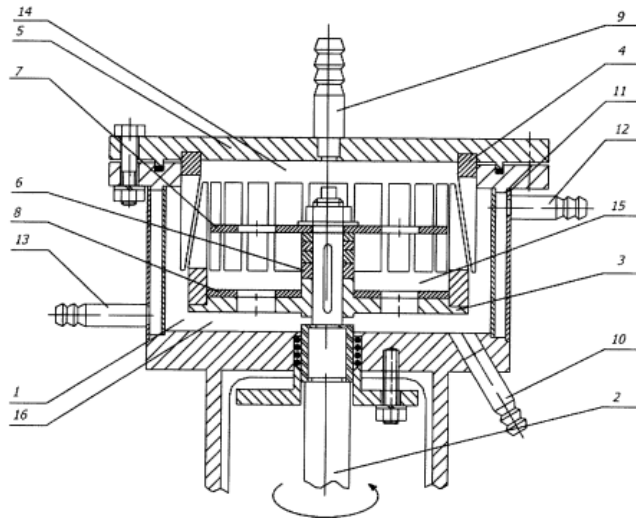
Багатосекційний роторно-пульсаційний апарат з робочими елементами ротора і статора у вигляді зубів: 1 – корпус; 2 – вал; 3 – ротор; 4 – статор; 5 – кришка; 6 – регулювальні шайби; 7, 8 – перегородки; 9, 10 – патрубки для введення та виведення компонентів; 11 – сорочка; 12, 13 – вхідний та вихідний патрубок холодоносія; 14 – робоча порожнина; 15 – нижня частина робочої області; 16 – зовнішня порожнина апарату
